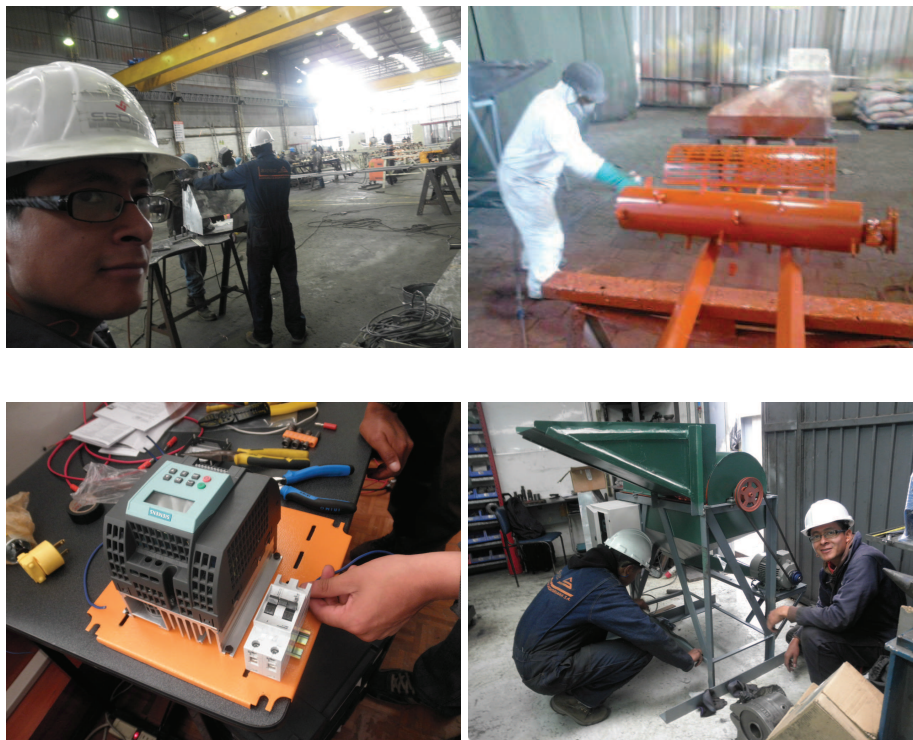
Soldado de las Tolvas y Armado del Sistema Reductor de Velocidades
